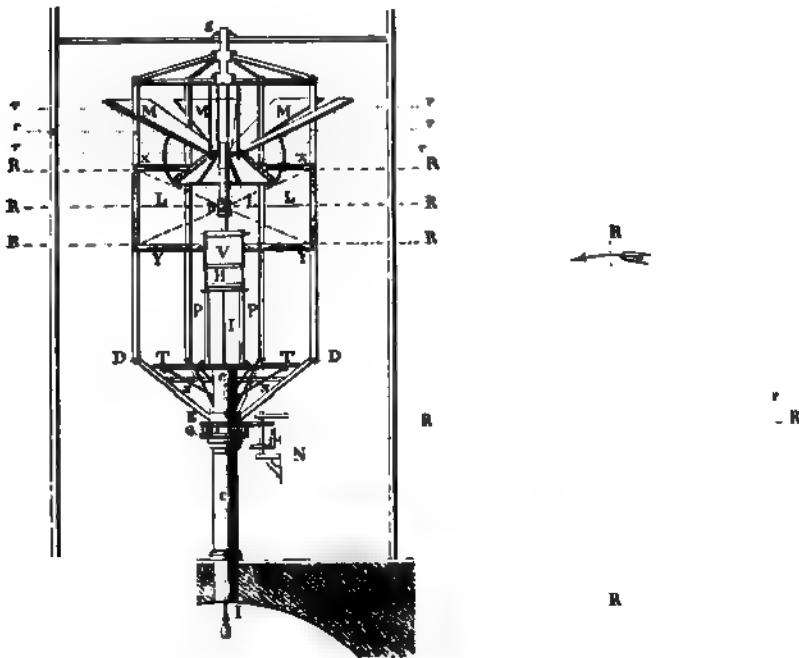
Premier appareil lenticulaire de Fresnel. Élévation et plan.
